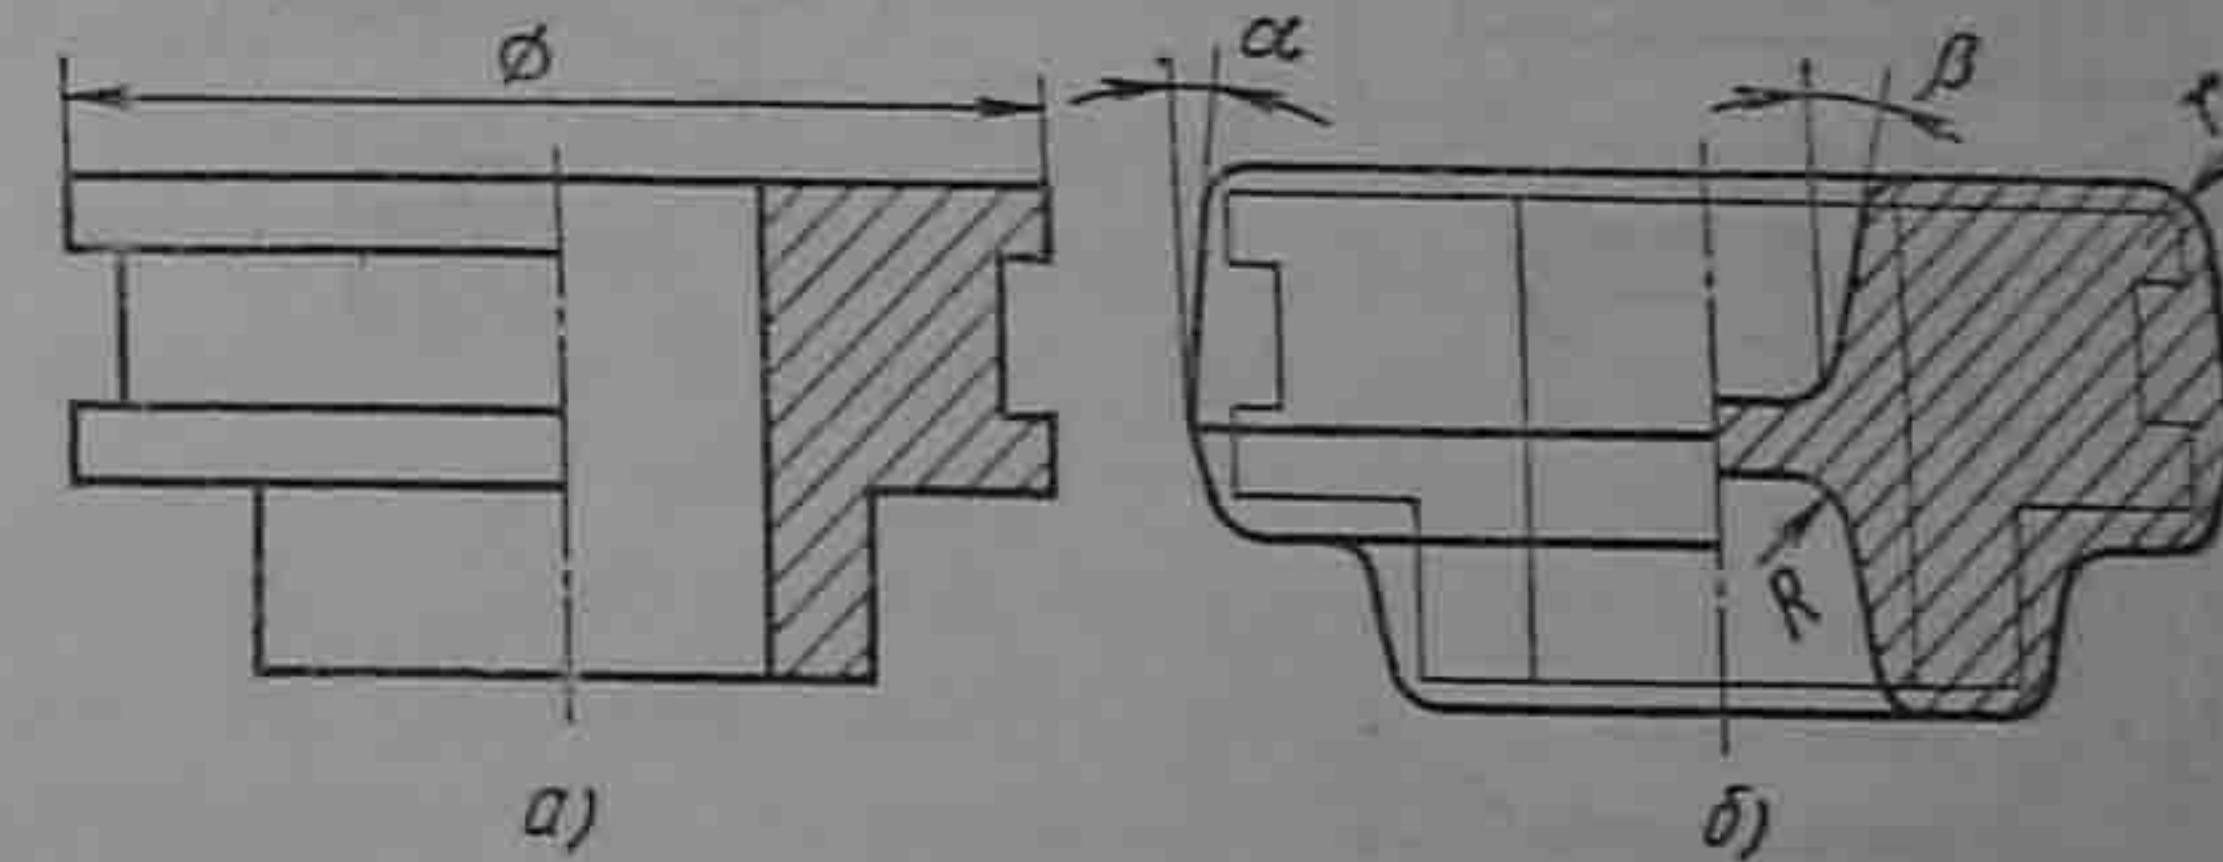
Пример составления чертежа поковки: а — деталь; б — поковка
